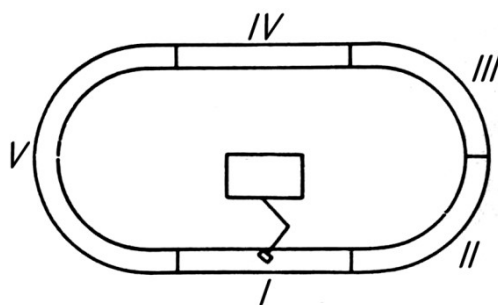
Схема пескометной линии для изготовления стержней: I – набивка стержня; II – удаление стержня из ящика III – подготовка ящика; IV – установка каркасов; V – подготовка новых ящиков.
